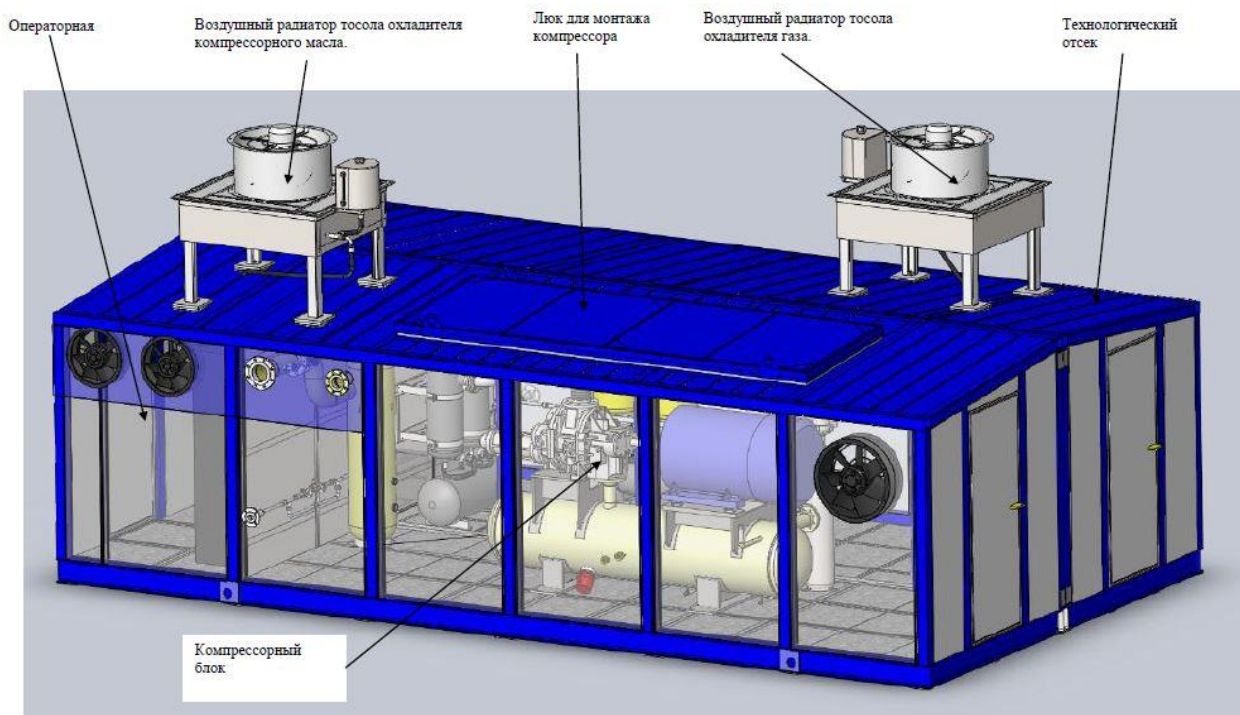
Внешний вид и основные элементы установки УПТГ
